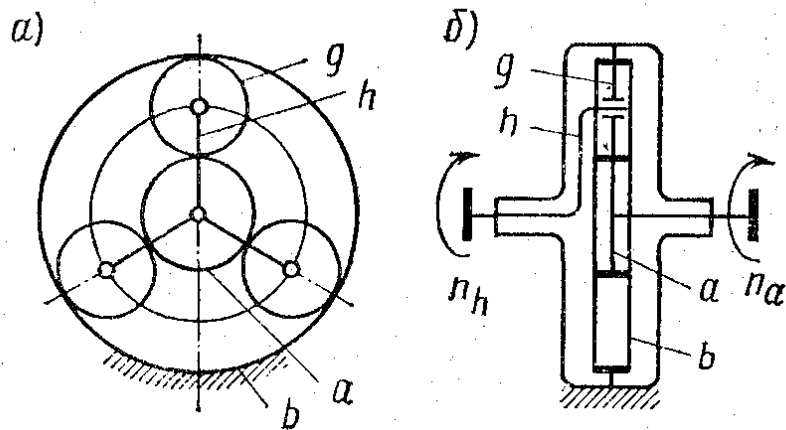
Схема одноступенчатого планетарного редуктора: а – центральное колесо с наружными зубьями, б – центральное колесо с внутренними зубьями, h – водило, g – сателлиты
